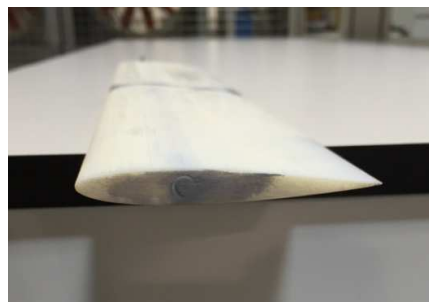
Orificio final tapado con la soldadura metálica en frío
